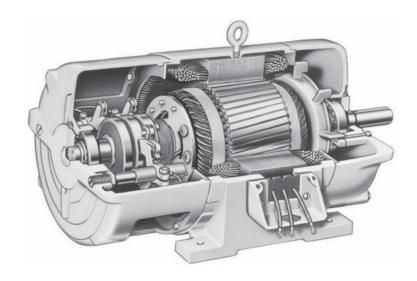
Motor con rotor devanado o anillos rozantes MagneTek.
